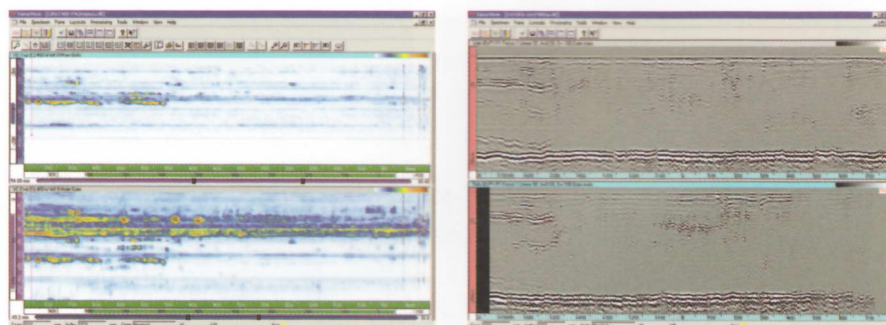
Объединенные В- и С-сканы и двойной TOFD-скан сварного шва.
